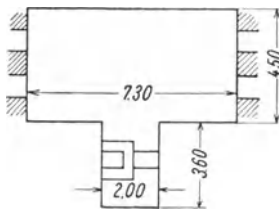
Grundriß einer Rohglaswanne mit Schöpfvorbau.
